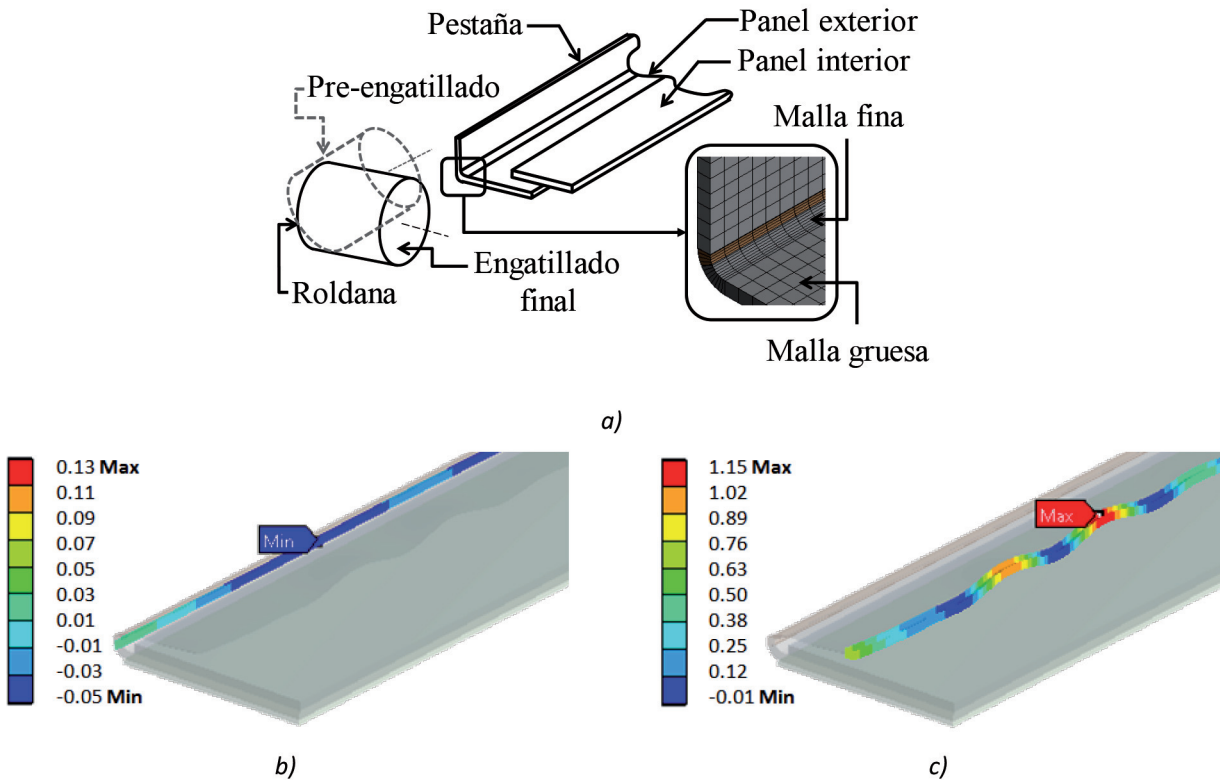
Modelado inicial: a) elementos del proceso de engatillado por roldana y características de malla; b) resultado de enrollamiento y desenrollamiento en chapa engatillada; y c) resultado de arruga en chapa engatillada
